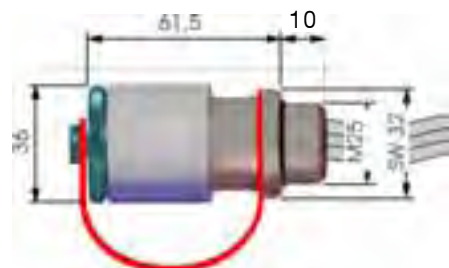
Maßbild Gerätestecker 2L Metall
